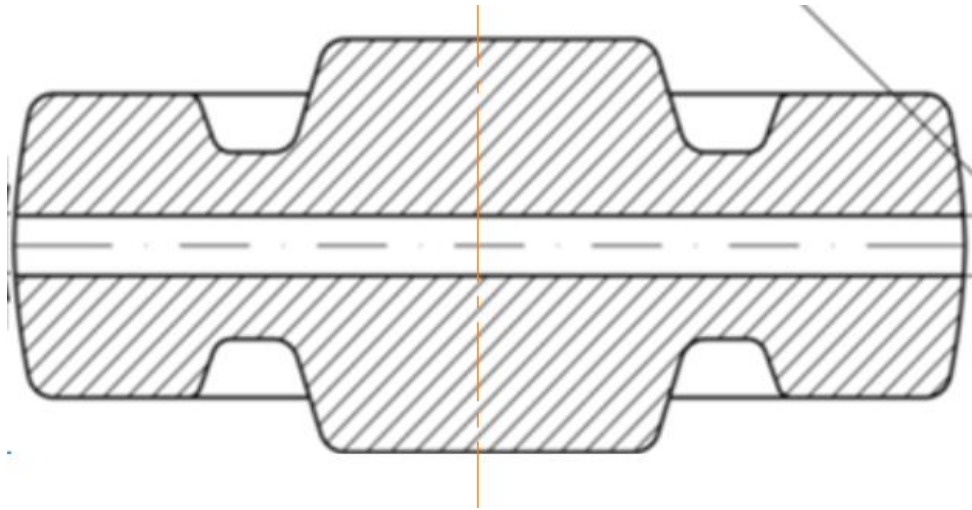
Недоштампівка поковки: H_n - висота недоштампованої частини поковки
